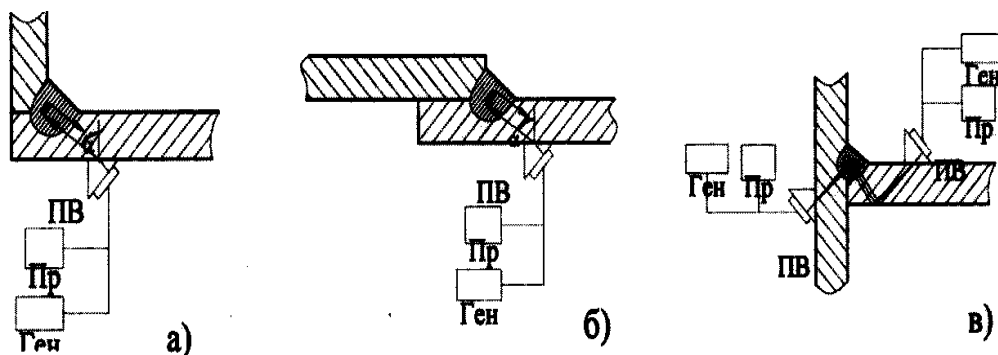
Схеми ультразвукового контролю зварних з'єднань
